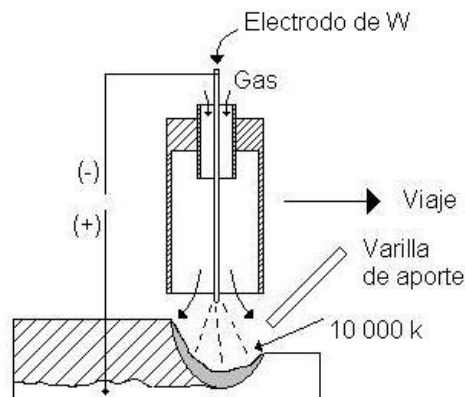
El arco se protege con gas en los procesos de soldadura con arco y gas inerte
